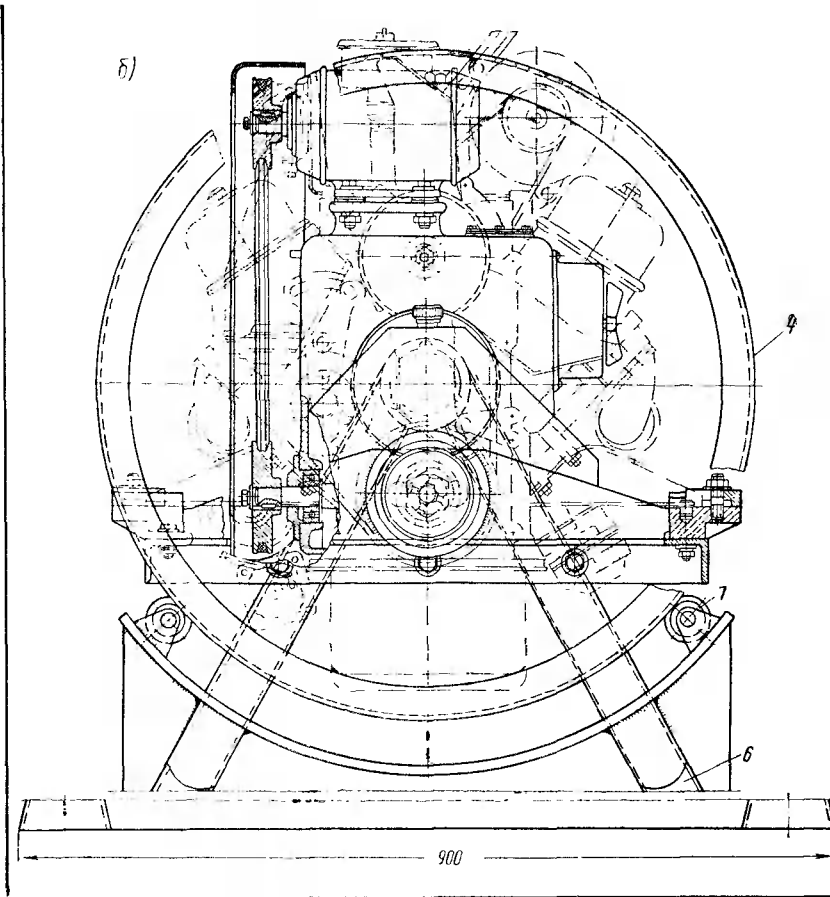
Стенд (тип I) для разборки и сборки V-образных двигателей:
